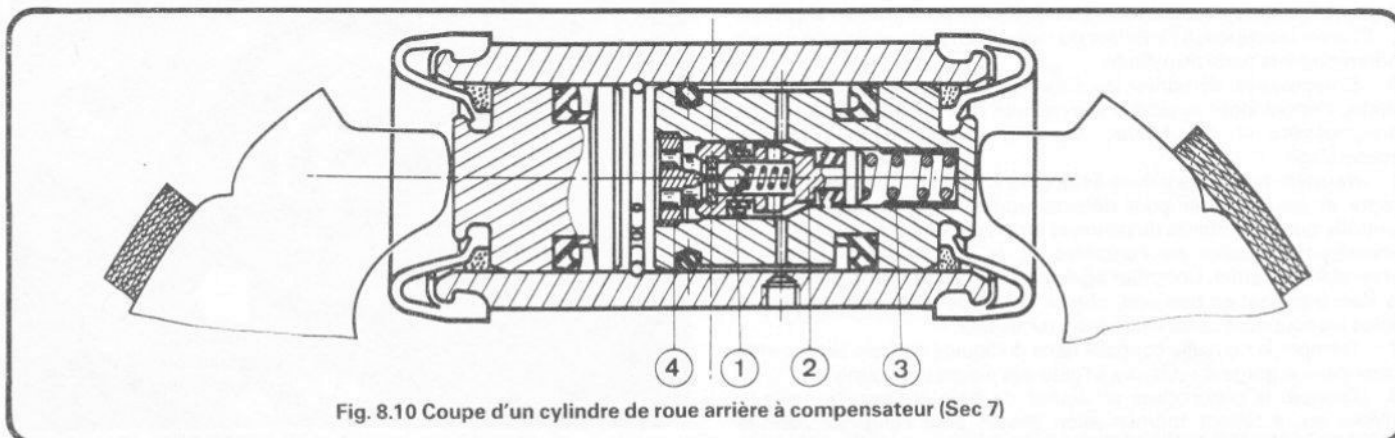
Coupe d'un cylindre de roue arrière à compensateur (Sec 7)
